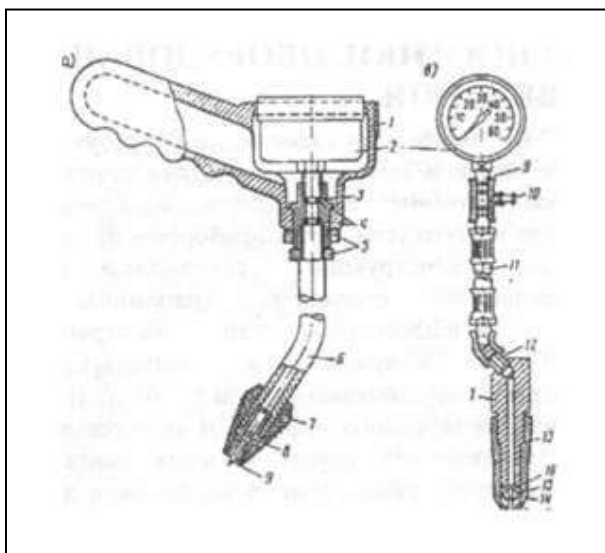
Компрессометры: *а* - для карбюраторных двигателей; *б* - для дизелей; 1 - корпус; 2 - манометр; 3 - штуцер; 4 - контргайки; 5 - трубка; 6 - резиновый наконечник; 7 - золотник; 8 - выпускной клапан; 9 - шланг; 10 - переходник; 11 - зажимная гайка; 12 - клапан; 13 - пружина клапана; 14 - седло; 15 - наконечник
